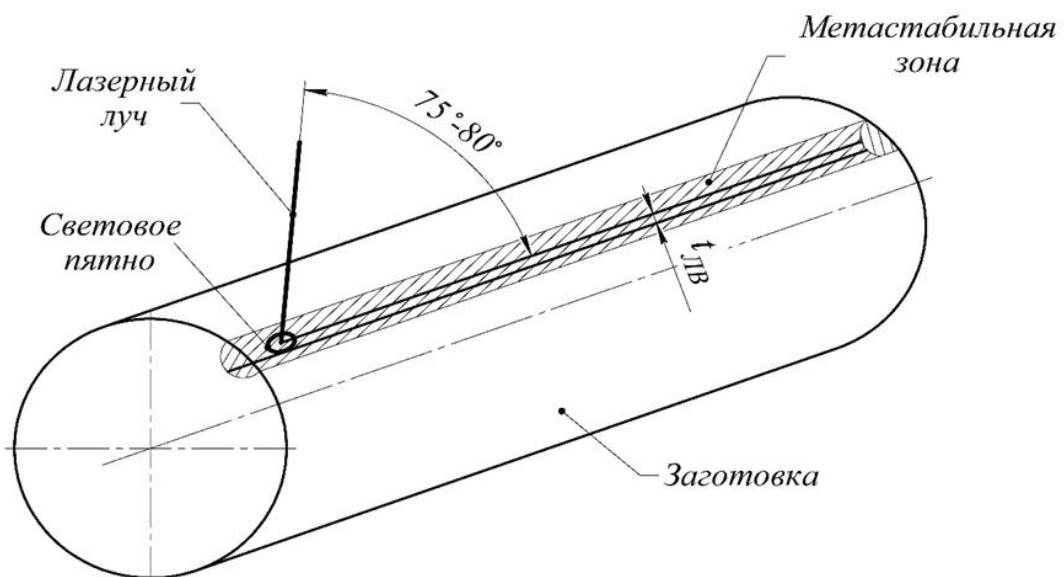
Способ обработки стальных заготовок с дроблением стружки на основе предварительного лазерного нагрева [57]
